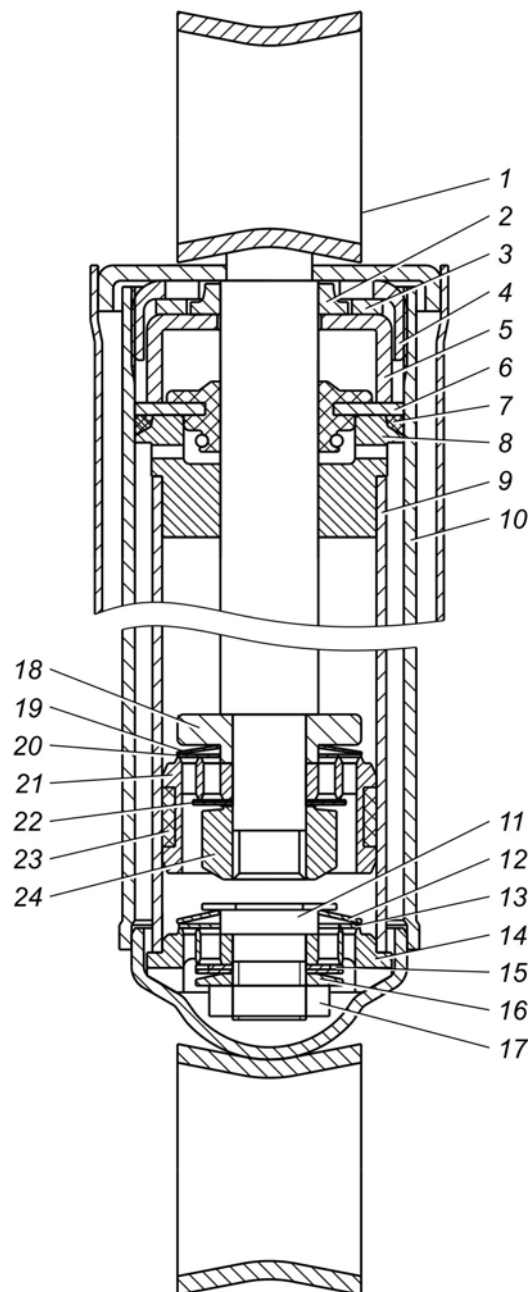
Амортизатор: 1 – шток с проушиной; 2 – пыльник; 3 – шайба; 4 – гайка резервуара; 5 – обойма сальника; 6 – манжета штока; 7 – кольцо; 8 – направляющая штока; 9 – цилиндр; 10 – резервуар; 11 – болт клапана сжатия; 12 – пружина перепускного клапана; 13 – тарелка перепускного клапана; 14 – корпус клапана сжатия; 15 – диски; 16 – тарелка ограничительная; 17 – гайка; 18 – тарелка ограничительная; 19 – пружина перепускного клапана; 20 – тарелка перепускного клапана; 21 – поршень; 22 – диски; 23 – поршневое кольцо; 24 – гайка
